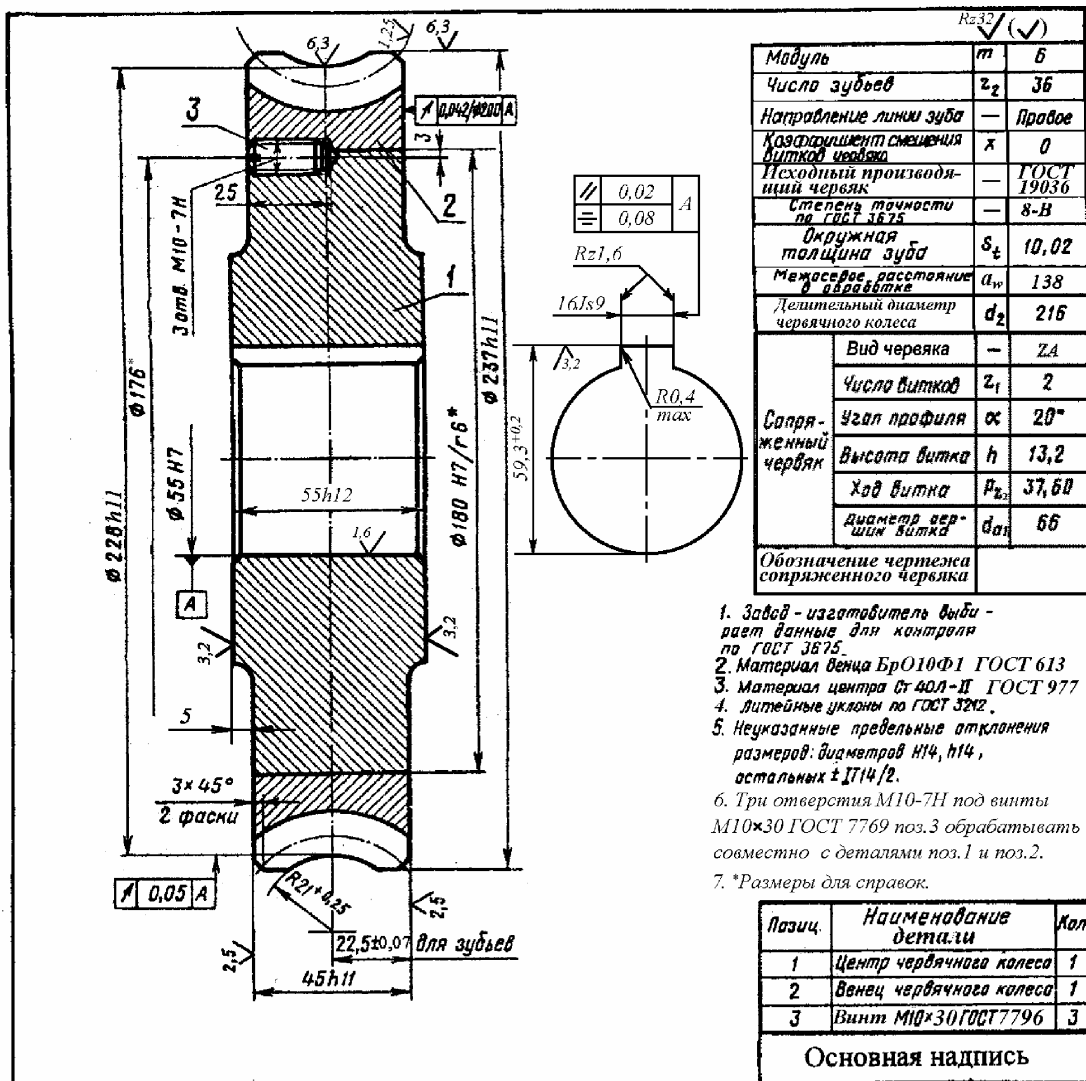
Рабочий чертеж червячного колеса в сборе
